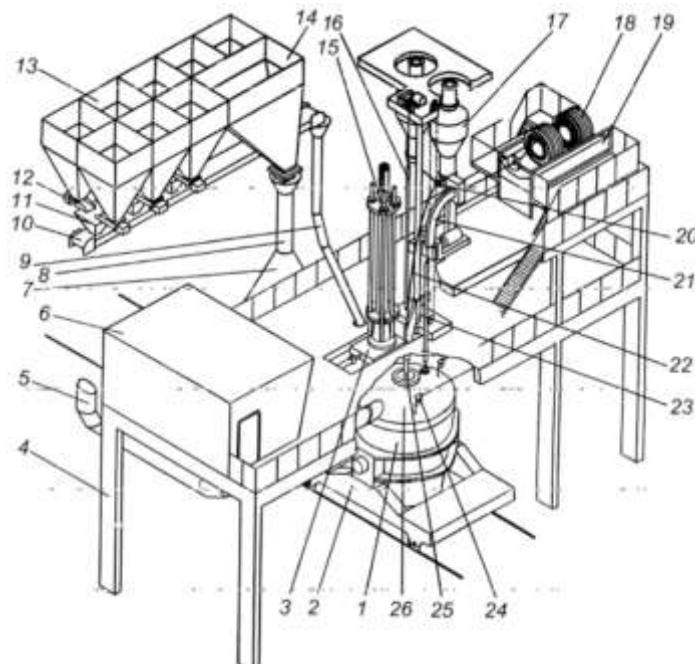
Общий вид агрегата для обработки стали в ковше порошкообразными реагентами: 1 - ковш; 2 - сталевоз; 3 - тележка для контейнера с фурмами; 4 - металлоконструкция; 5 - газоход; 6 - пост управления; 7 -
